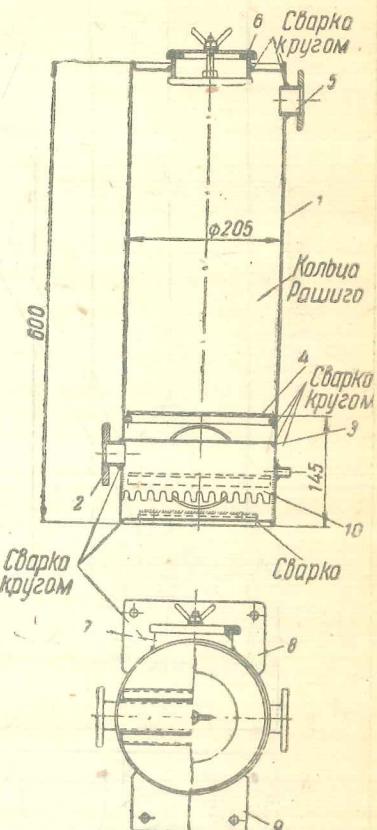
Поверхностный очиститель конструкции НИКФИ
